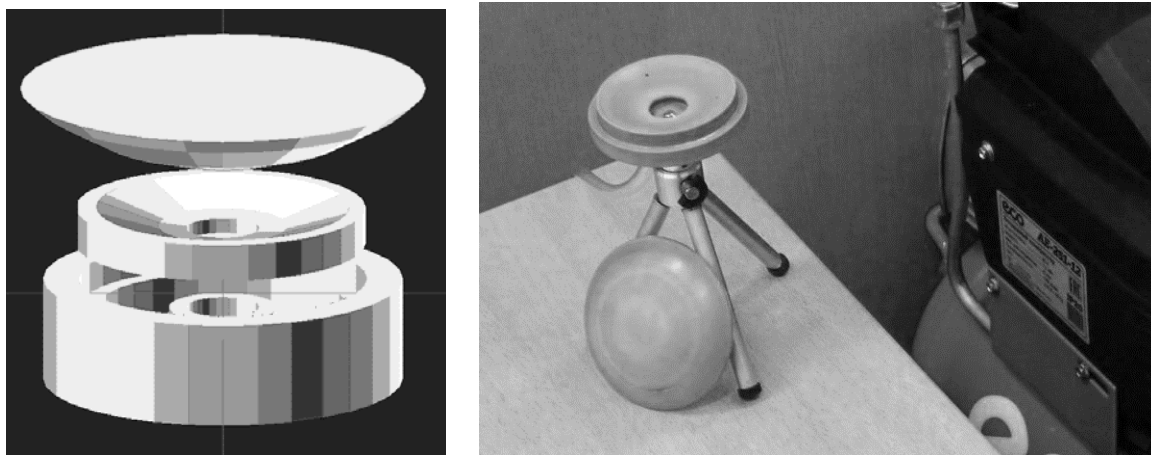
Сборочный чертеж аэродинамического подвеса и фото установки в сборе
